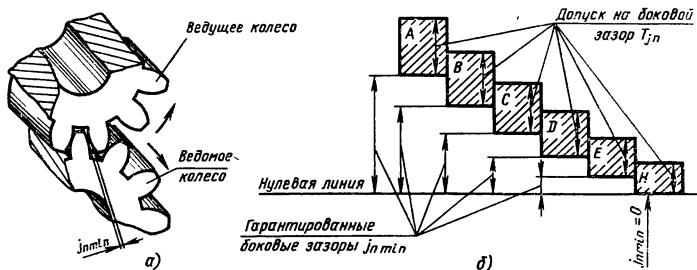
Боковой зазор зубчатого зацепления (а), виды сопряжений и допуски на боковой зазор (б)
